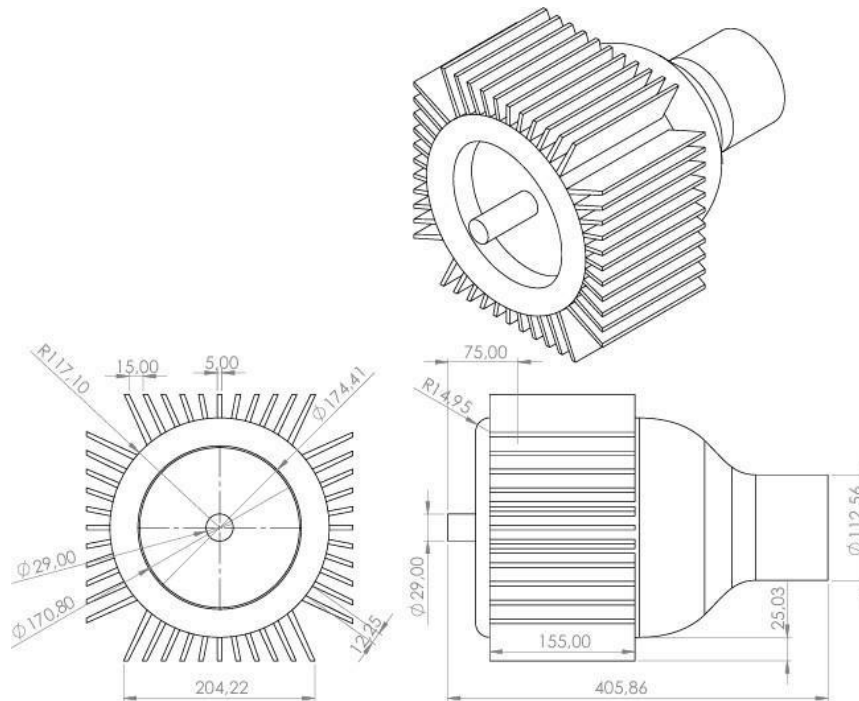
Explode view* Desain Motor BLDC AFPM
